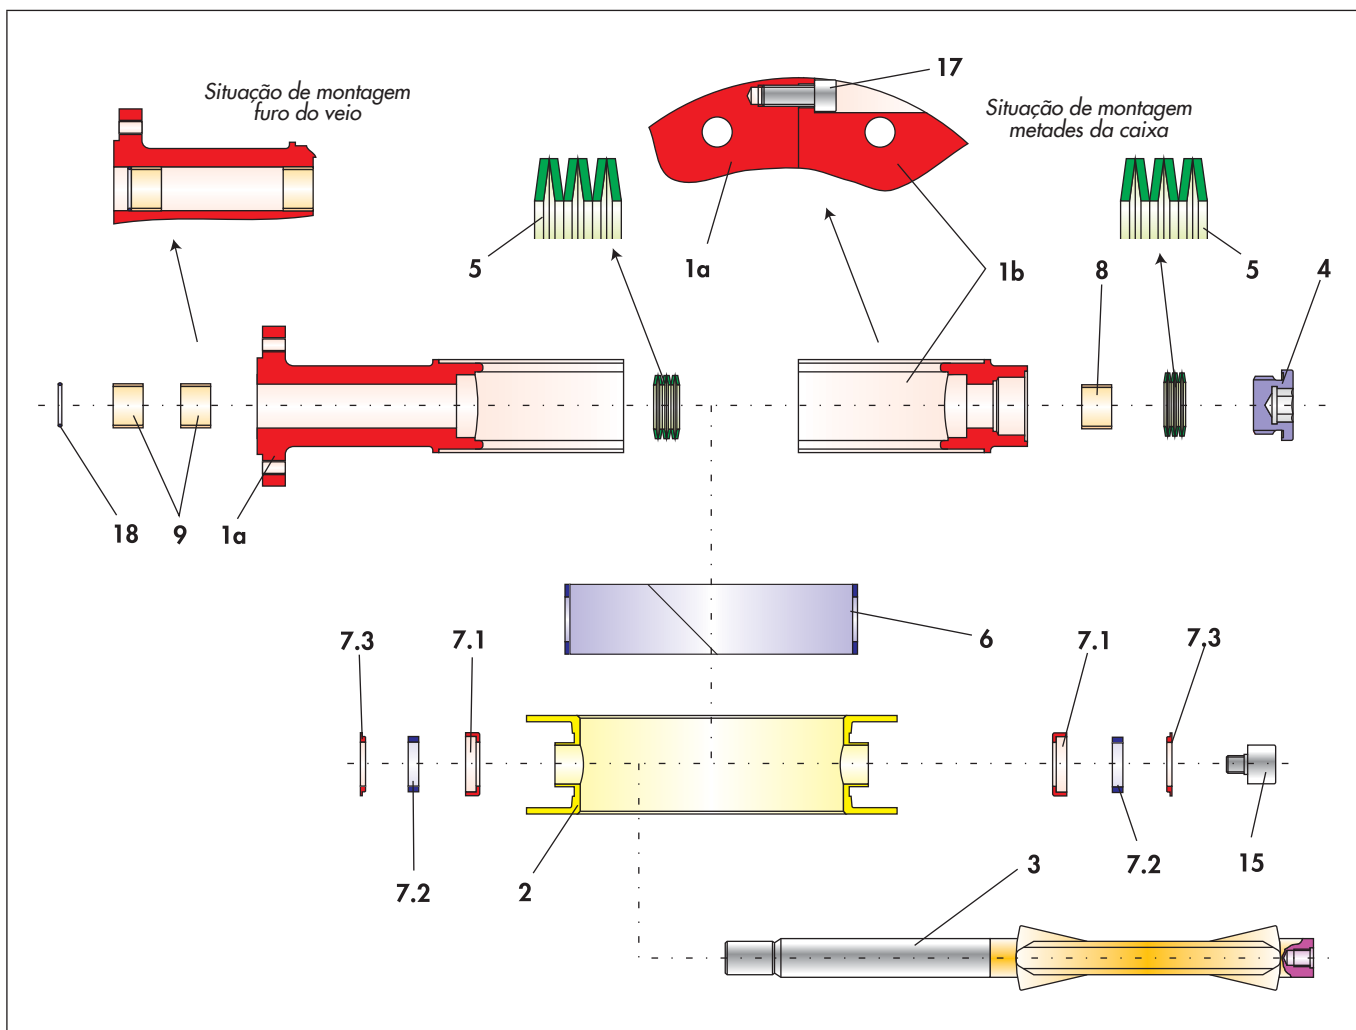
Desenho explodido da válvula borboleta BR 10e
